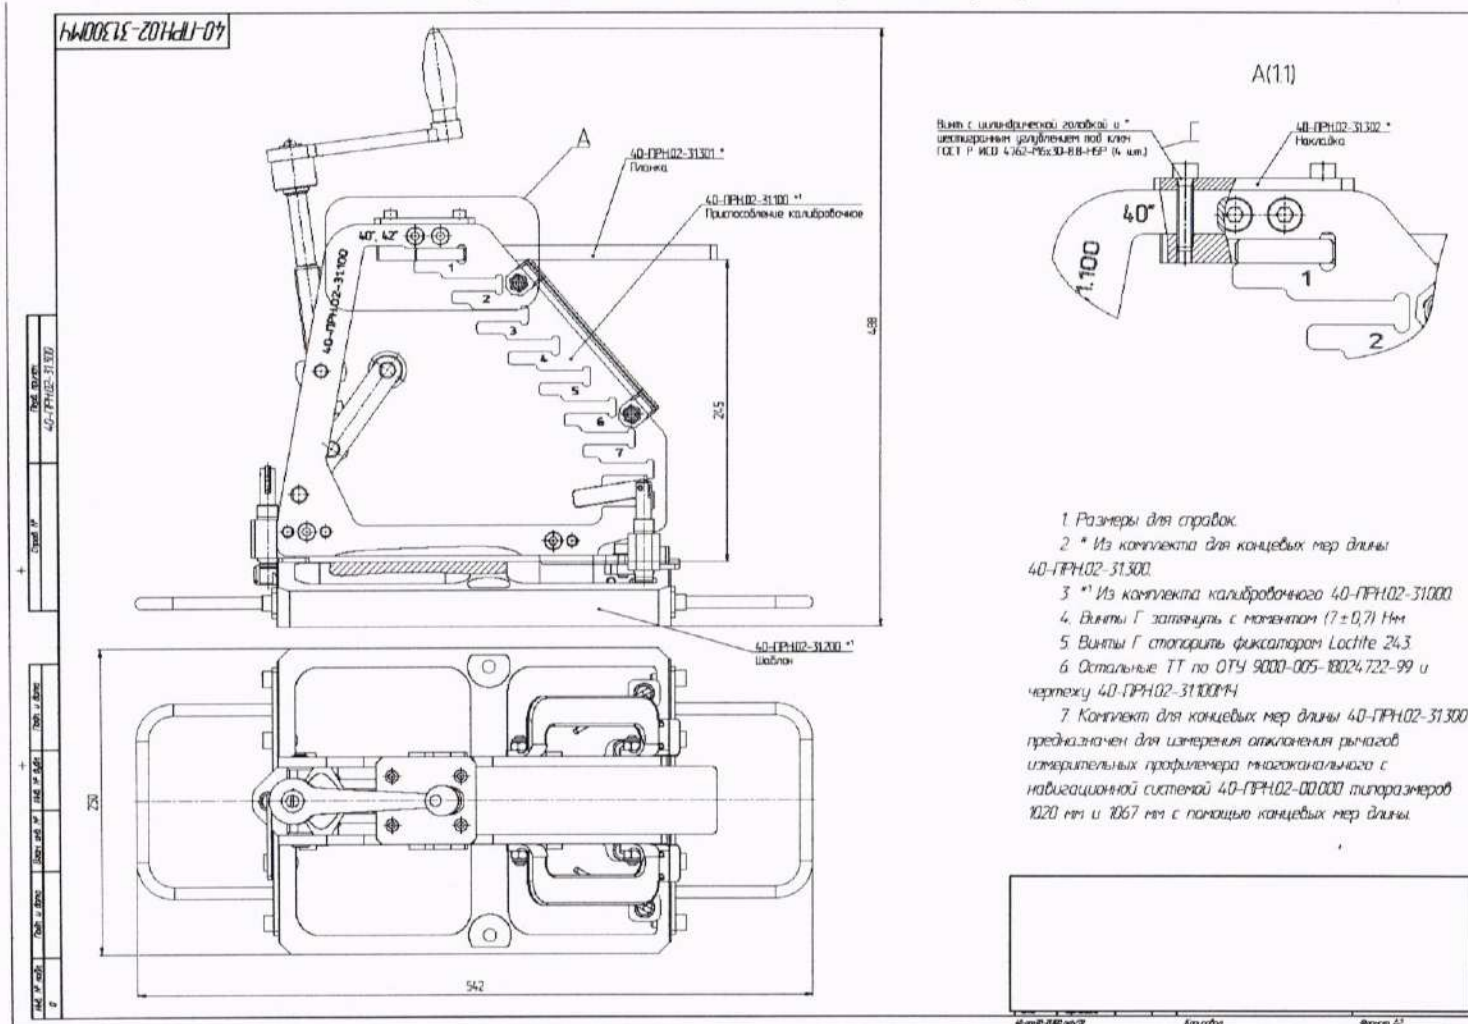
Чертеж планки установленной на калибровочное устройство
